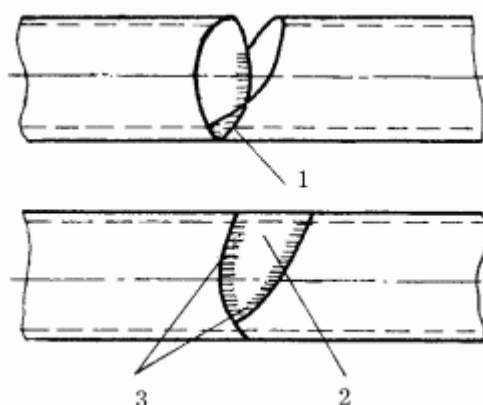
Комбинированный способ сварки: 1 – нижняя часть шва; 2 – вставка; 3 – верхняя часть шва.
